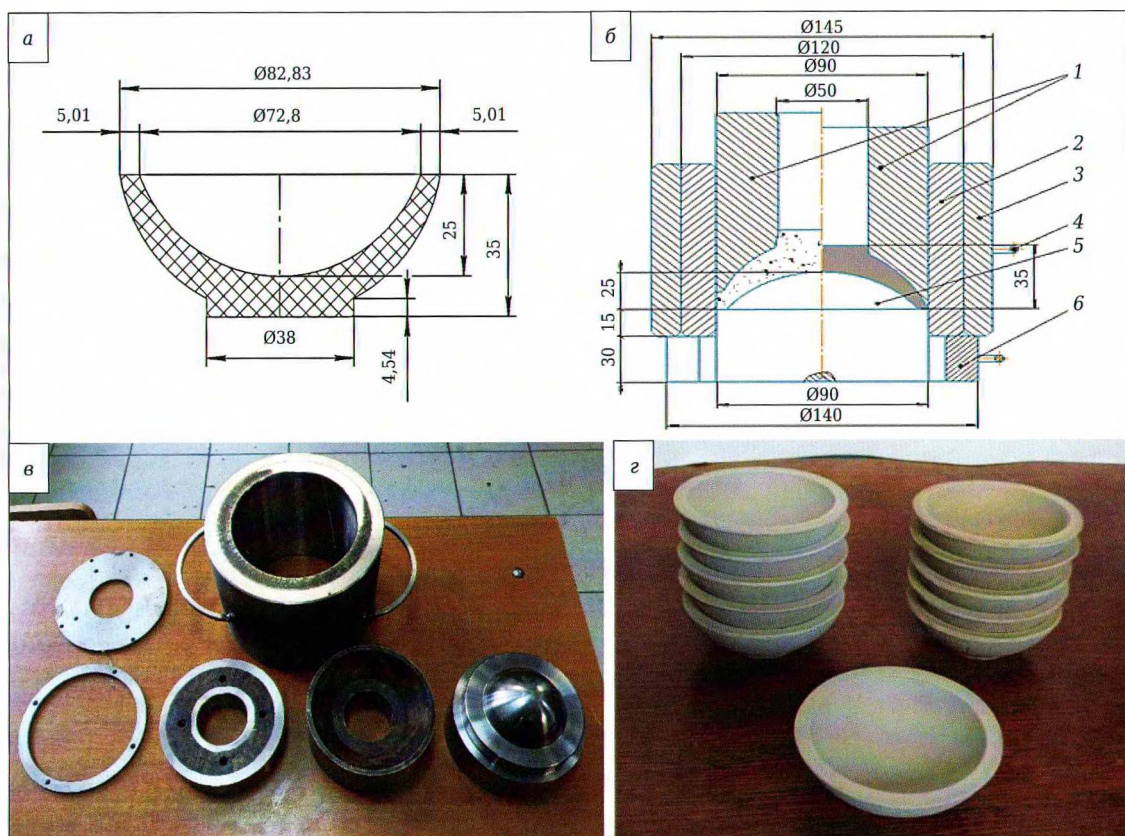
Конструкция изделий — шербера (а), пресс-формы (б) и технологическая оснастка — пресс-форма (в) для формования заготовок шерберов (з): 1 — пуансон верхний; 2 — матрица; 3 — бандаж; 4 — ручка; 5 — пуансон нижний; 6 — кольцо упорное
